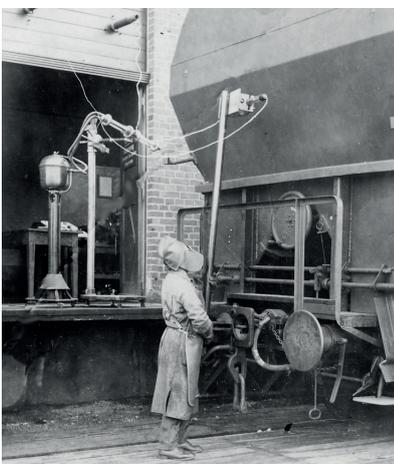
Untersuchung der Schweißnähte an einem Schüttgutwagen
